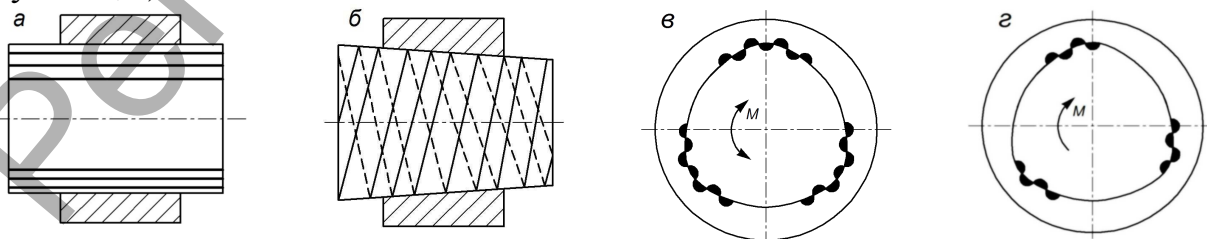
Схемы лазерного упрочнения деталей цилиндрических (*а*) и конических (*б*) ПМС реверсивного (*в*) и нереверсивного (*г*) типов
